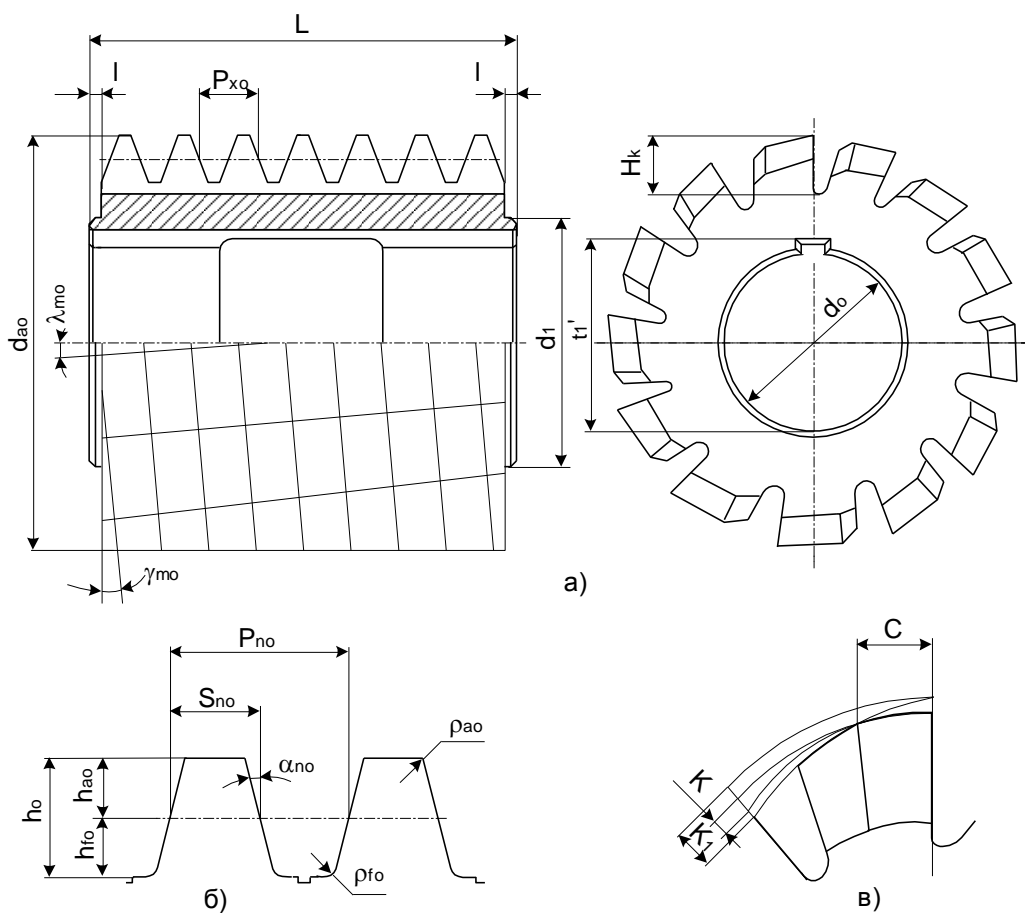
Червячная зуборезная фреза: а - общий вид; б - размер профиля в нормальном сечении; в - элементы затылования зубьев
